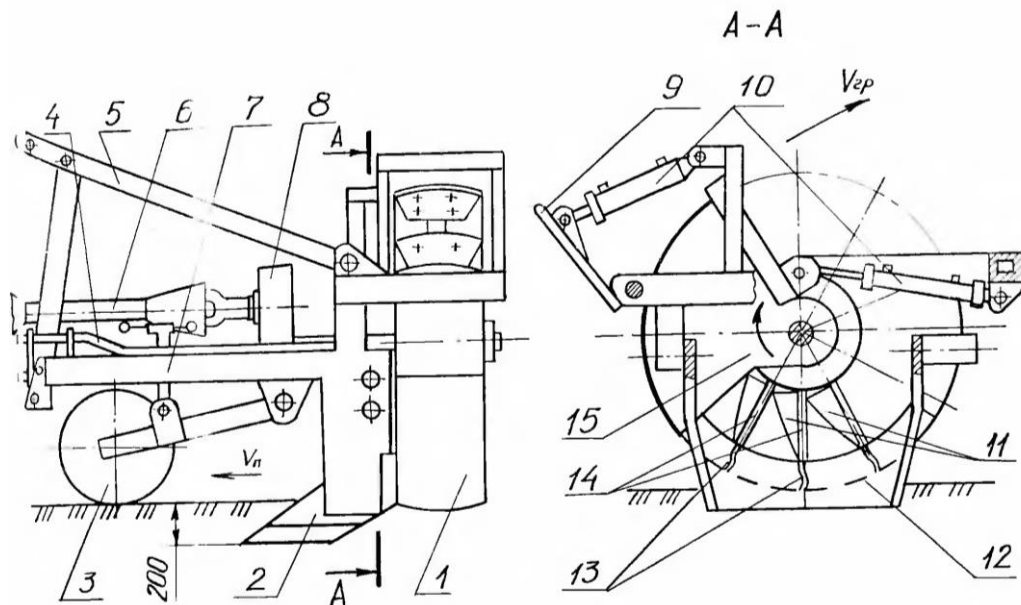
Конструктивно-технологічна схема експериментальної роторно-лопатевої машини для насипки валів-терас: 1 – ротор; 2 – підкопуючий робочий орган; 3 – опорний каток; 4 – гідросистема; 5 – навіска; 6 – карданна передача; 7 – рама; 8 – редуктор; 9 – направляючий щит; 10 – гідроциліндри; 11 – відрізнi ножі; 12 – днище; 13 – розвантажувальні лопаті; 14 – важелі; 15 – рухомий кожух.
